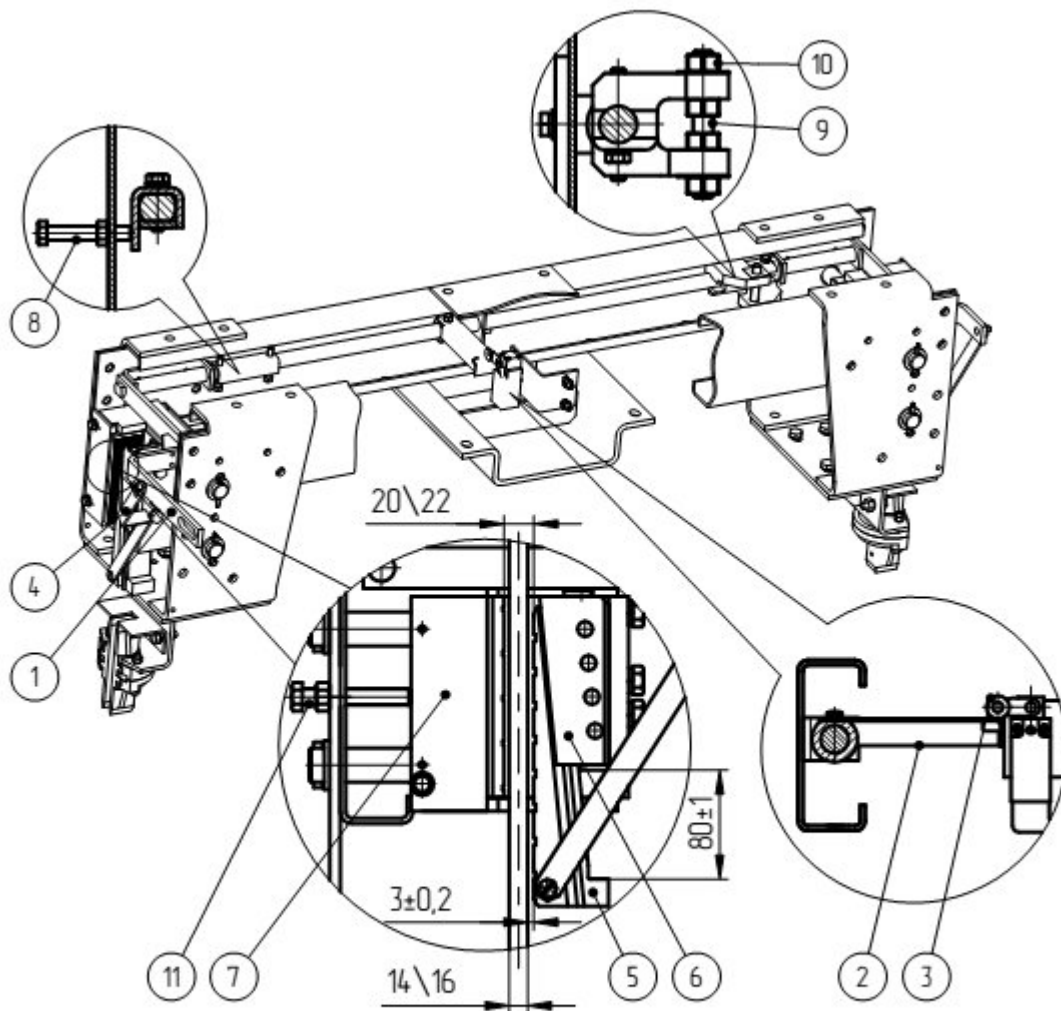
Ловитель одностороннего действия: 1 - рычаг троса; 2 - планка; 3 - выключатель; 4 - тяга; 5 - клин; 6 - колодка; 7 - колодка тормозная; 8 - болт регулировочный; 9 - шпилька; 10 - гайка; 11 - болт регулировочный.
